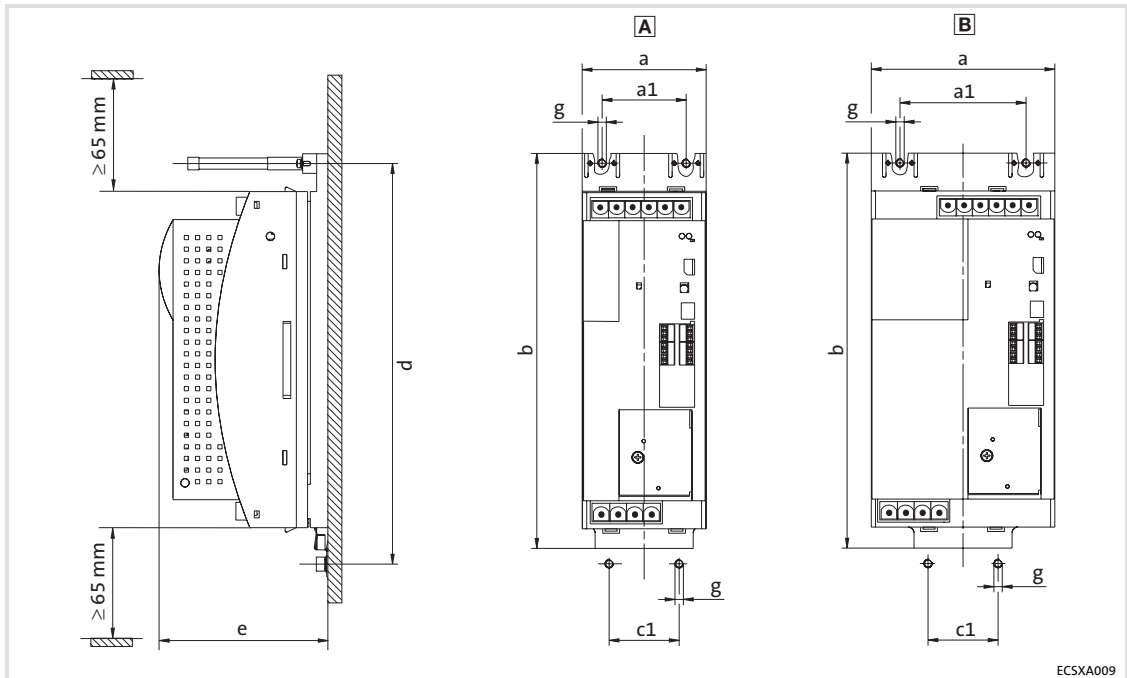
Dimensioni per il montaggio con tecnica "Cold-Plate"
